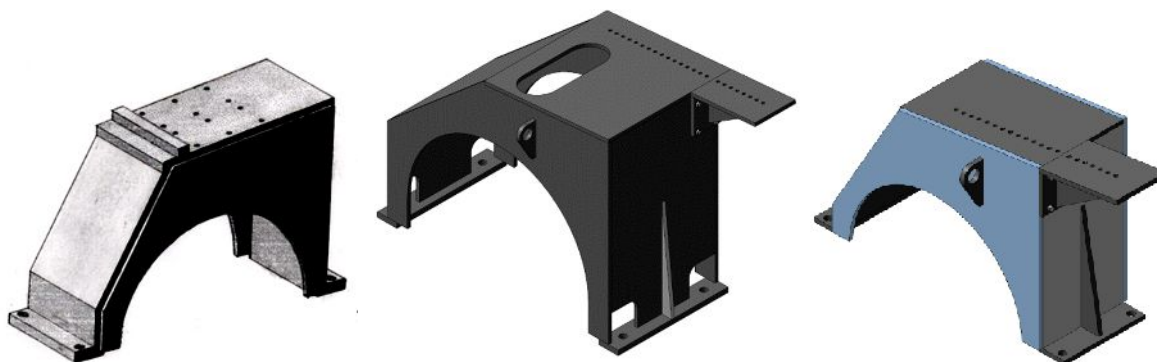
Конструкции сменных технологических наладок для установки станка на корпуса подшипников
